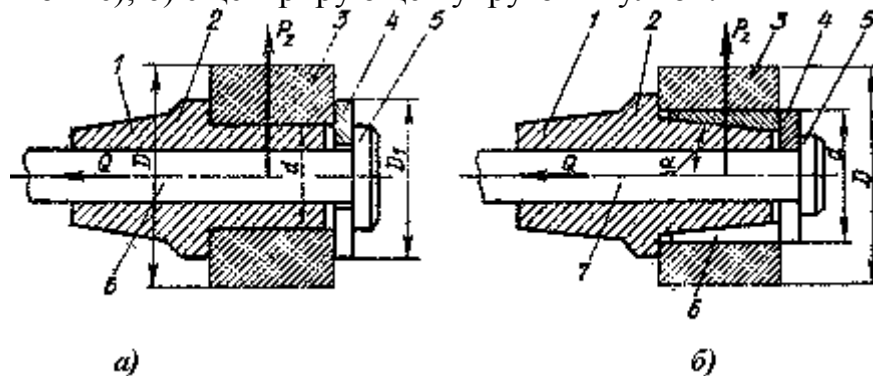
Конструкции оправок: а — гладкая оправка; б — оправка с разрезной втулкой.
